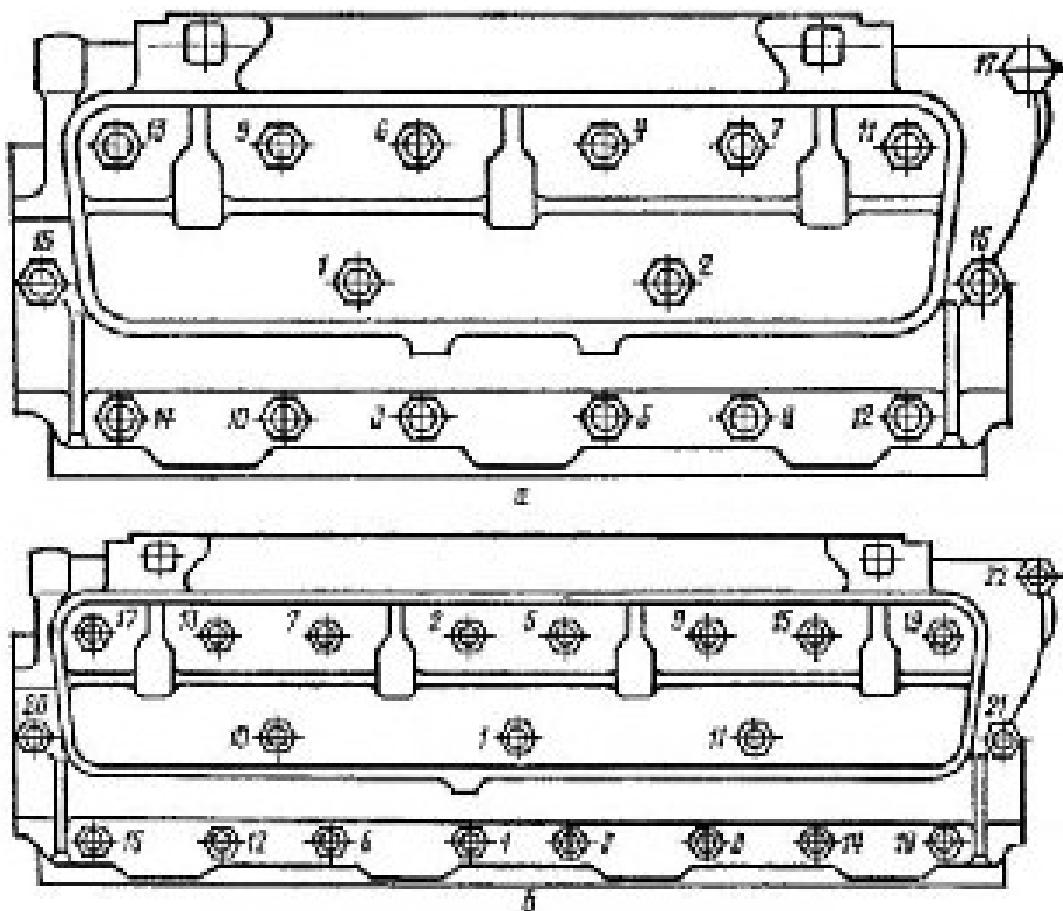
Последовательность затяжки гаек крепления головки цилиндров: а — дизеля СМД-66; б — дизеля СМД-36.
